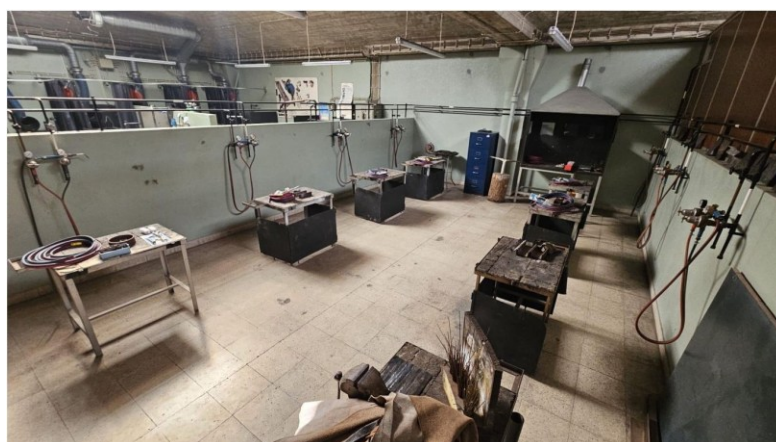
Área de soldadura Oxiacetilénica e Brasagem
